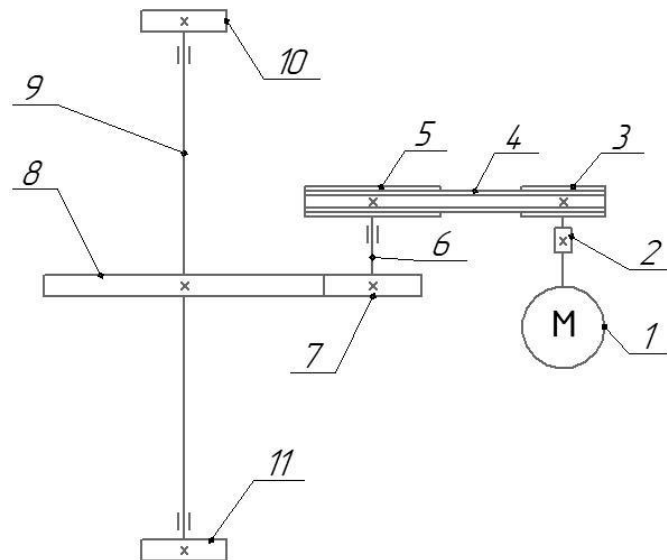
Кінематична схема привода круглов'язальної машини: 1-електродвигун; 2- запобіжна пружна зубчаста муфта; 3 та 5 - ведучий та ведений шківни клинопасової передачі; 4 - паси; 6 – проміжний вал; 7 - ведуча шестерня; 8 - зубчасте колесо; 9 - приводний вал; 10 та 11 - шестерні
